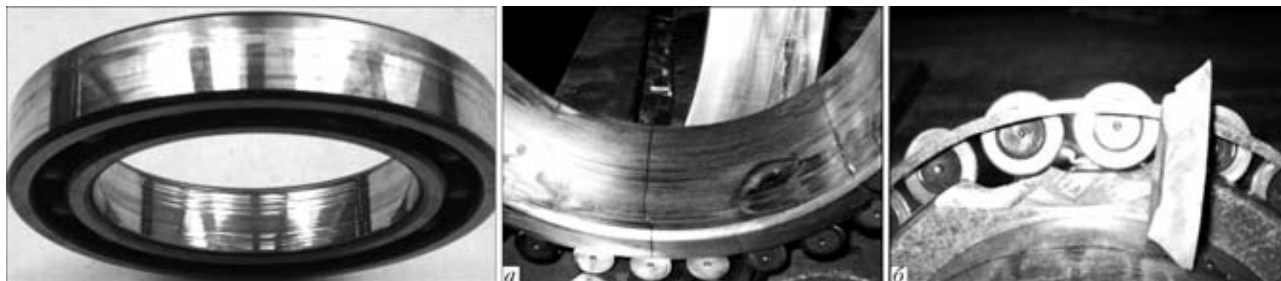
Следы проворачивания колец подшипника вследствие ослабления его посадки
